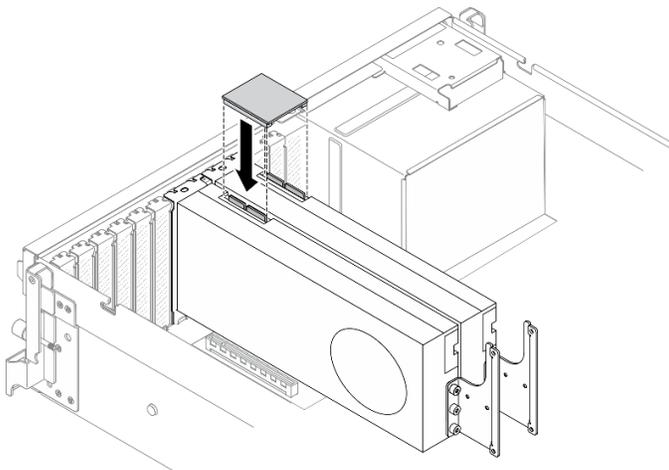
Installazione del Bridge di collegamento dell'adattatore GPU
